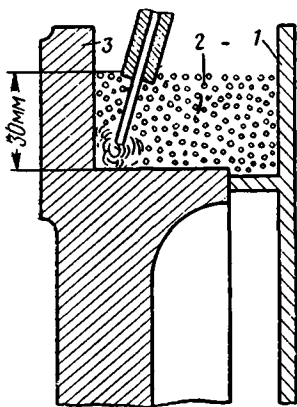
Флюсоудерживающее приспособление, применяемое при наплавке подшпнниковых щитов;
